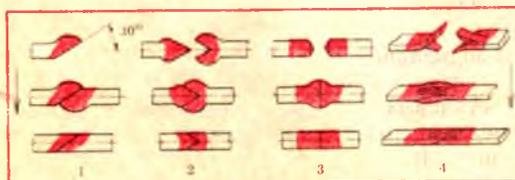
Способы сварки: 1 — внахлест; 2 — в разруб; 3 — встык; 4 — вращеп
